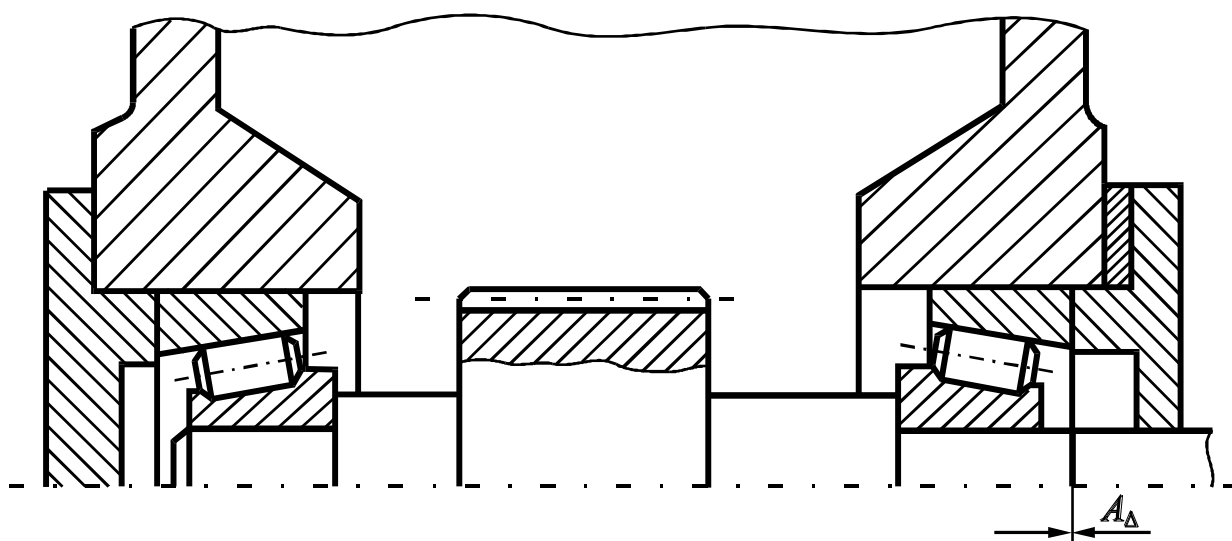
Сборочный узел вала шестерни цилиндрического редуктора
